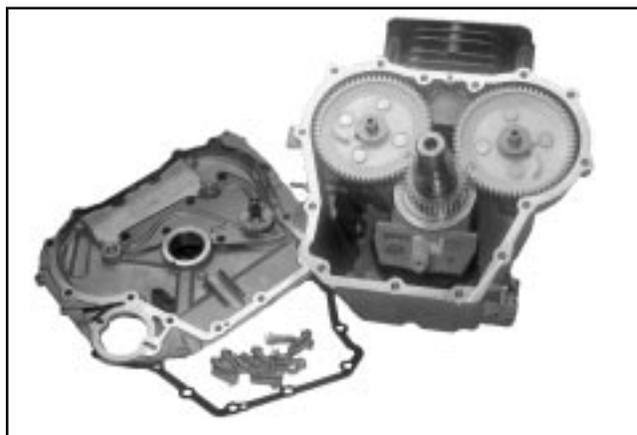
Plaque de fermeture et joint retirés du carter.
